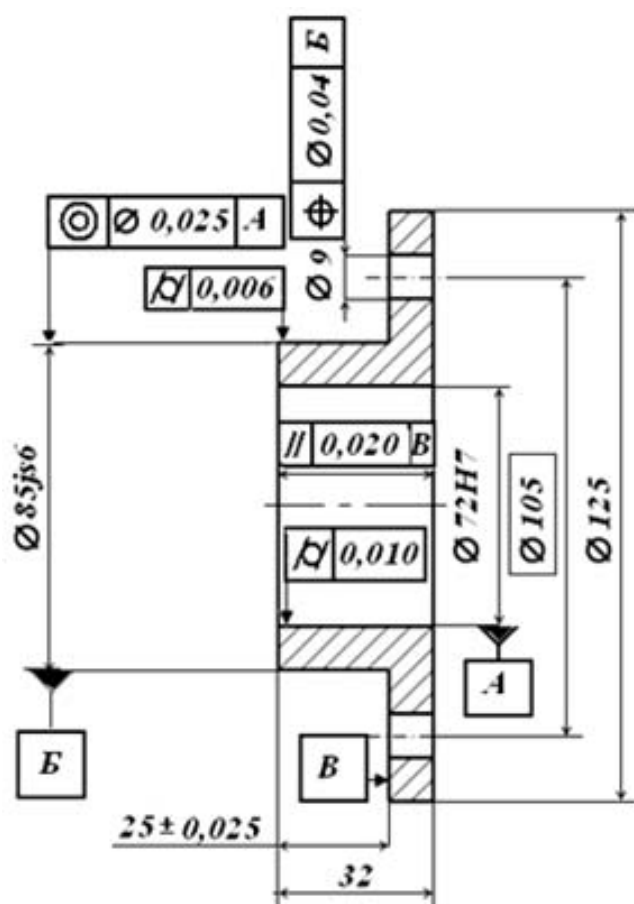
Ескіз стакана з зазначенням баз і допусків форми і розташування поверхонь
